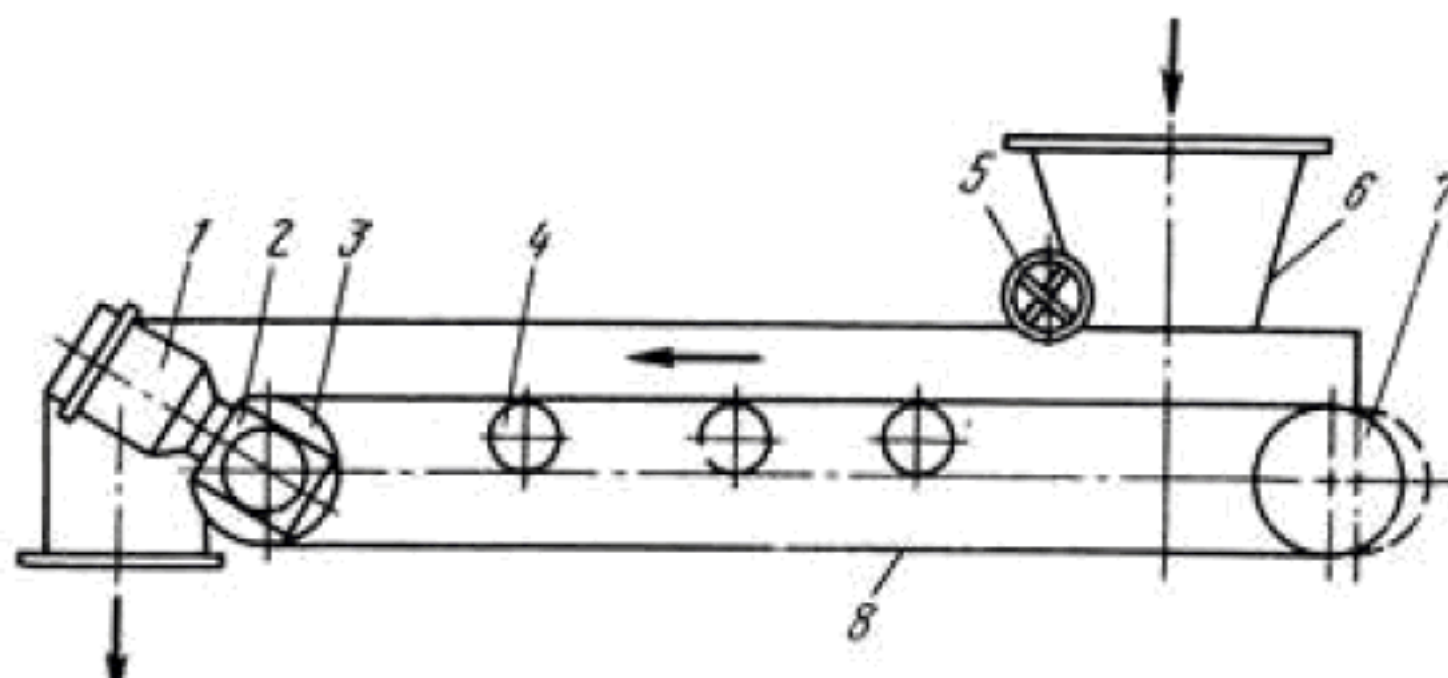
Живильник стрічковий типу ПЛ: 1 – електродвигун; 2 – механізм руху стрічки; 3 – привідний барабан; 4 – роликоопори; 5 – шибер з механізмом підйому; 6 – бункер; 7 – натяжний барабан; 8 – стрічка [5]
